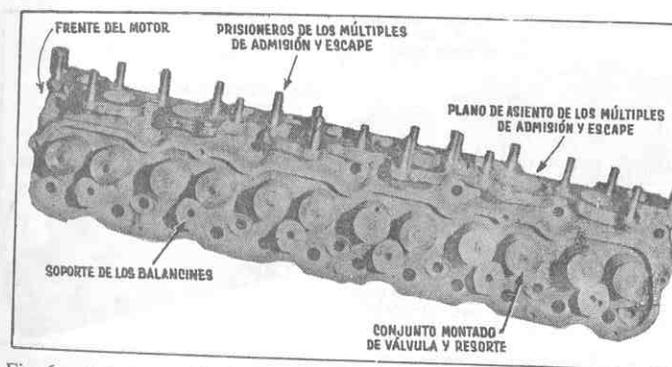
Tapa de cilindros del motor 221 SP. Vista desde arriba.
